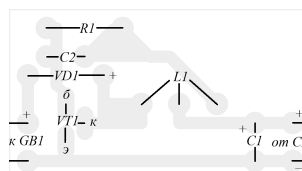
Эскиз монтажной платы преобразователя напряжения от СБ для QRP-радиостанции. Вид со стороны установки деталей
